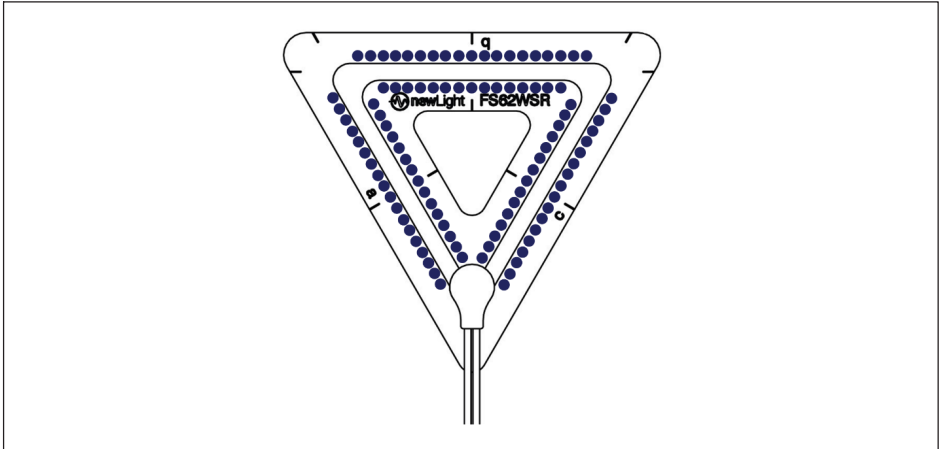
Modèle de soudage terminé de la FS62WSR BRD.
